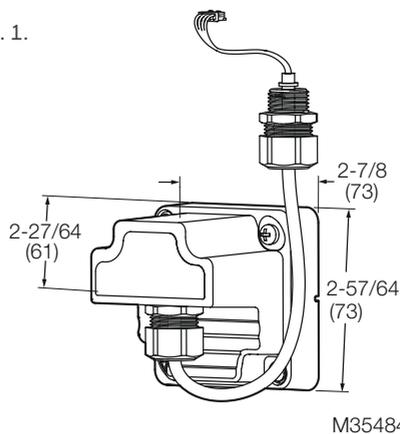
Dimensões do Módulo de Pressão em pol. (mm).
